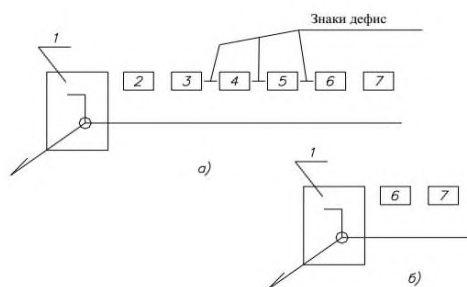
Структура условного обозначения сварного шва
